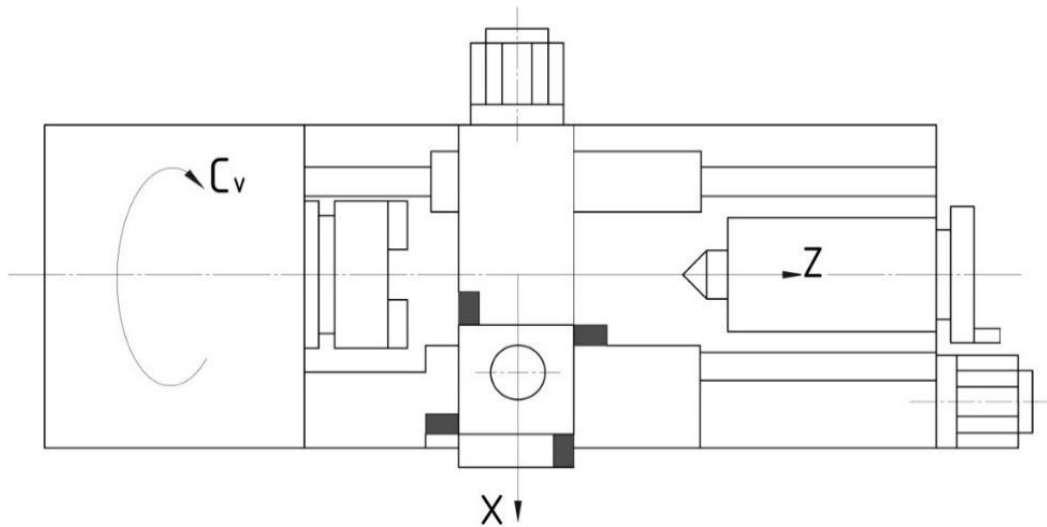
Компоновка токарного верстата (Варіант 1)
